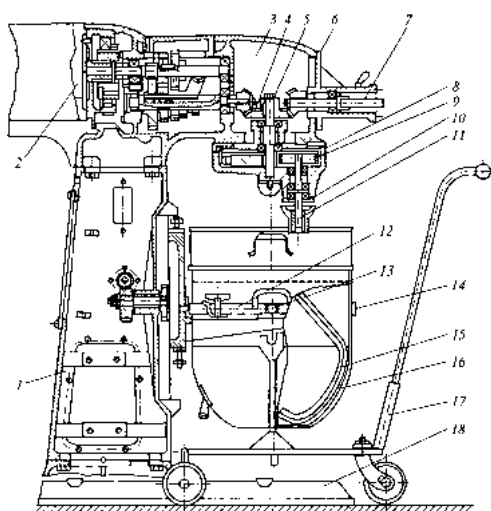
Вибрирующая машина МВ-60: 1 - станина; 2 - электродвигатель; 3 - коробка скоростей; 4 - коническое колесо; 5 - вертикальный вал; 6 - корпус вала отбора мощности; 7- вал отбора мощности; 8- нижняя крышка; 9- сателлит; 10- рабочий валик; 11 - штифт; 12- подставка; 13- фиксатор; 14- кольцо бачка; 15- сбиватель; 16- бачок; 17-тележка; 18- плита
